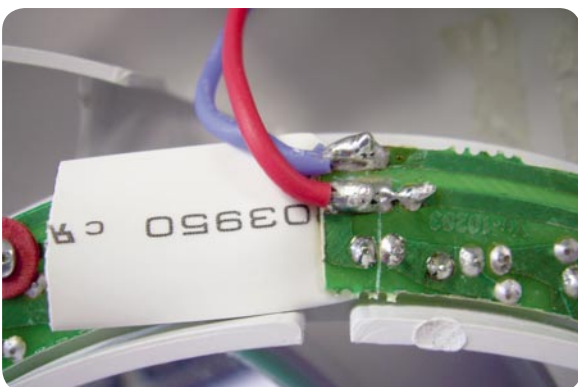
Angeklebt – schlampige Lötstellen, Kabel nicht fixiert
